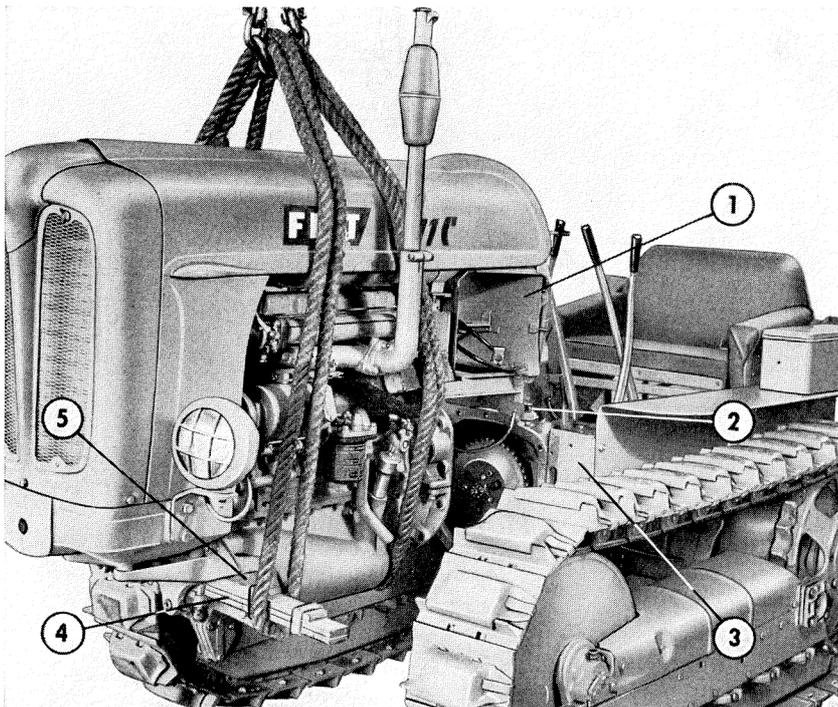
Dépose du moteur équipé de sa carrosserie et de la suspension avant.
